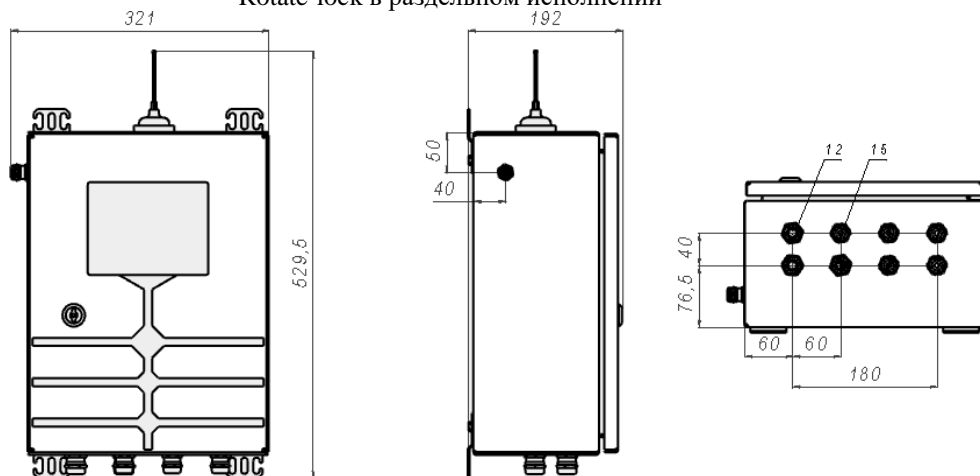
Габаритные и присоединительные размеры модуля выносного
